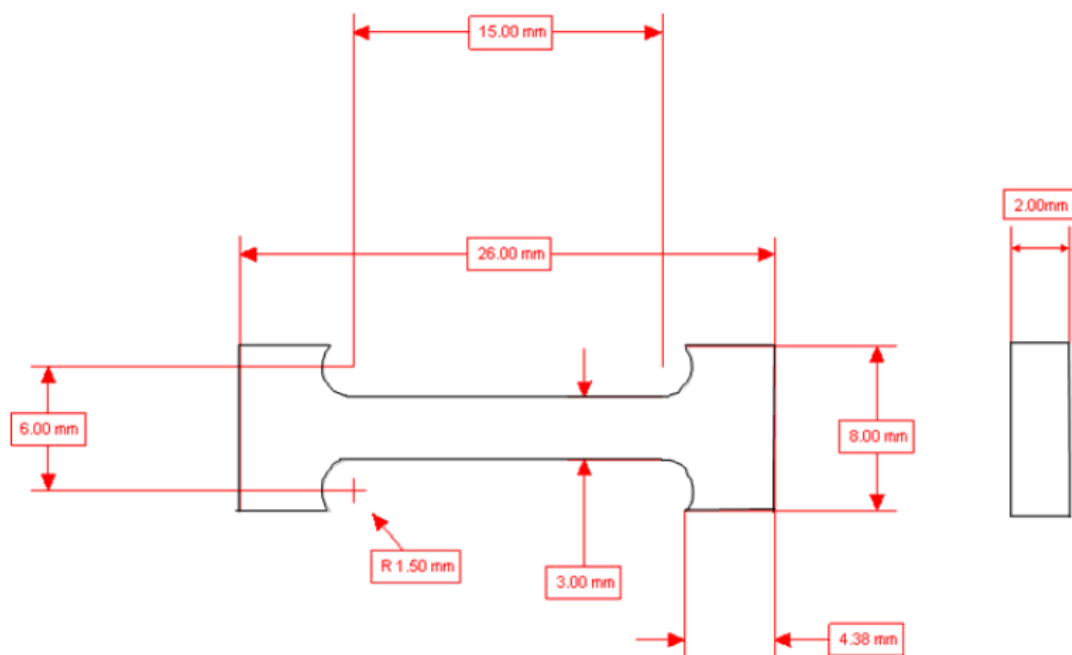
Plano de las dimensiones de las muestras de acero AISI 316L para los ensayos de tracción/SSRT.
